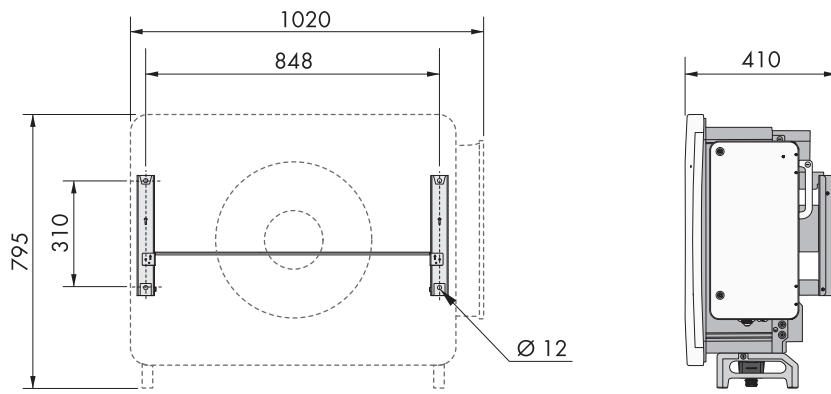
Dimensioni del supporto di montaggio (indicazioni in mm)
